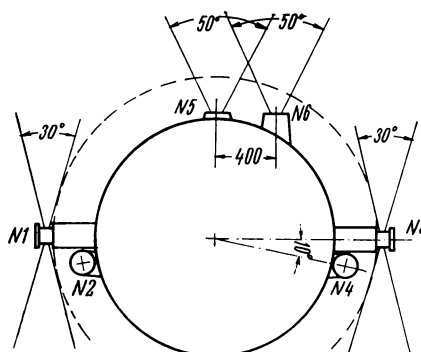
Схема установки камер на станции «Луноход-1» (вид сверху)
